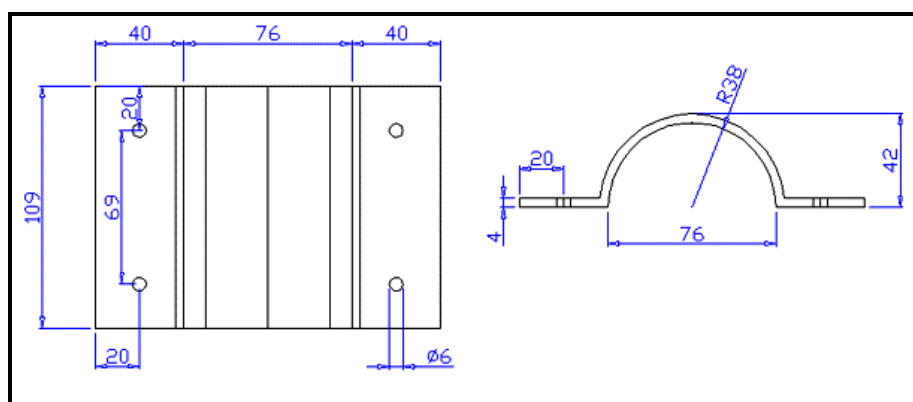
Esquema de construção da braçadeira do cilindro.
